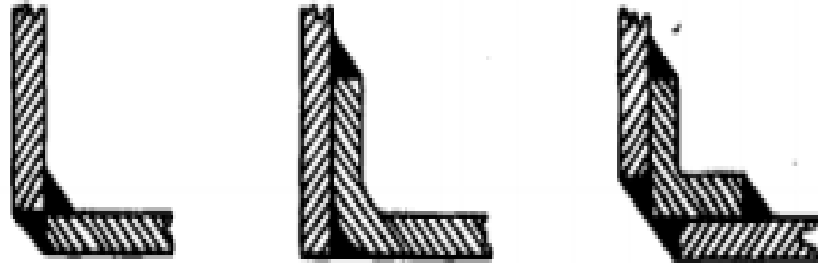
Soldadura de placas para tanques rectangulares. Fuente: [15]
